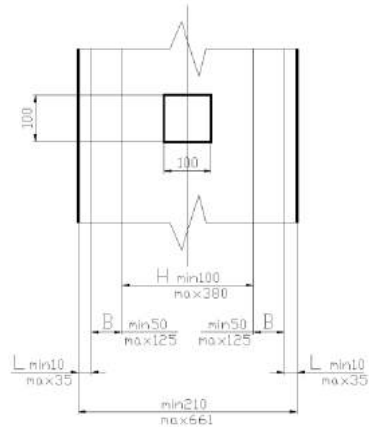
Схема расположения квадратных отверстий в исходной заготовке профиля.
